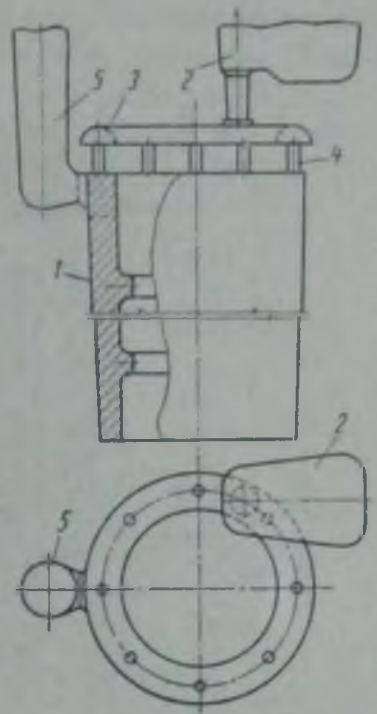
Дождевая литниковая система для отливки чугуна цилиндра:
